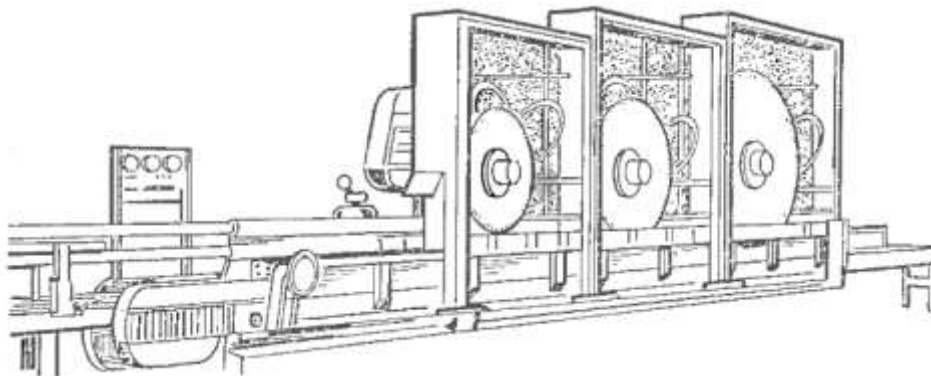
Багатовальний дисковий верстат СЦМ 60/3.
